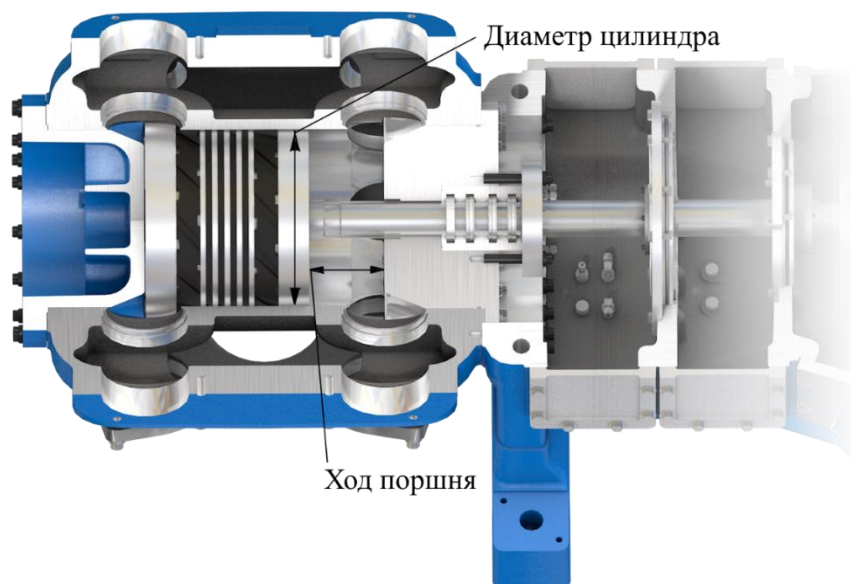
обозначение диаметра цилиндра и хода поршня
